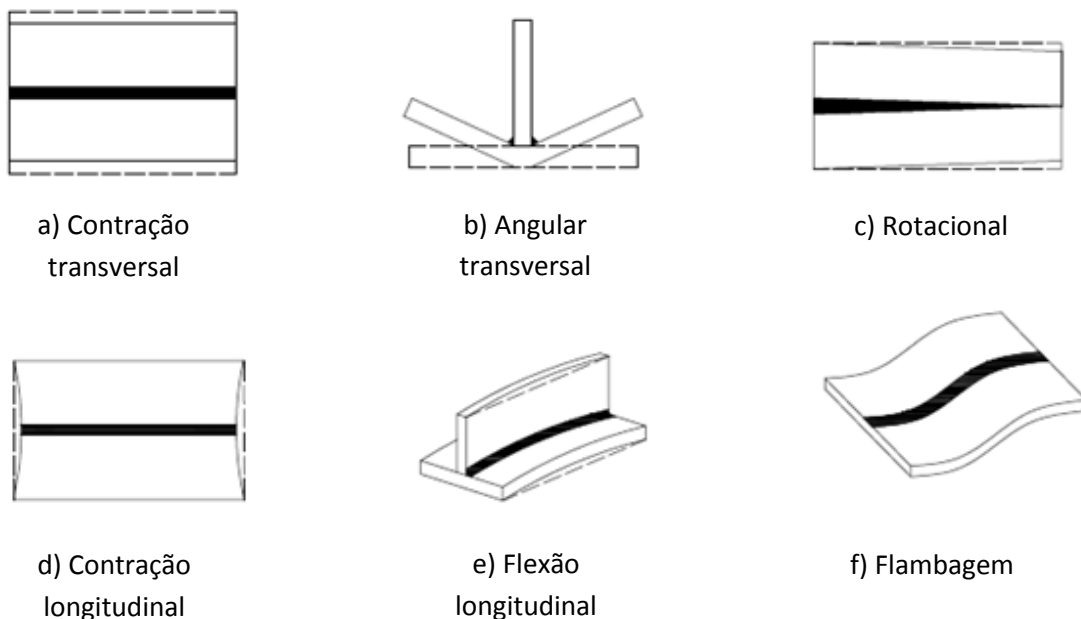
Principais tipos de distorções devido ao processo de soldagem⁽¹²⁾.
